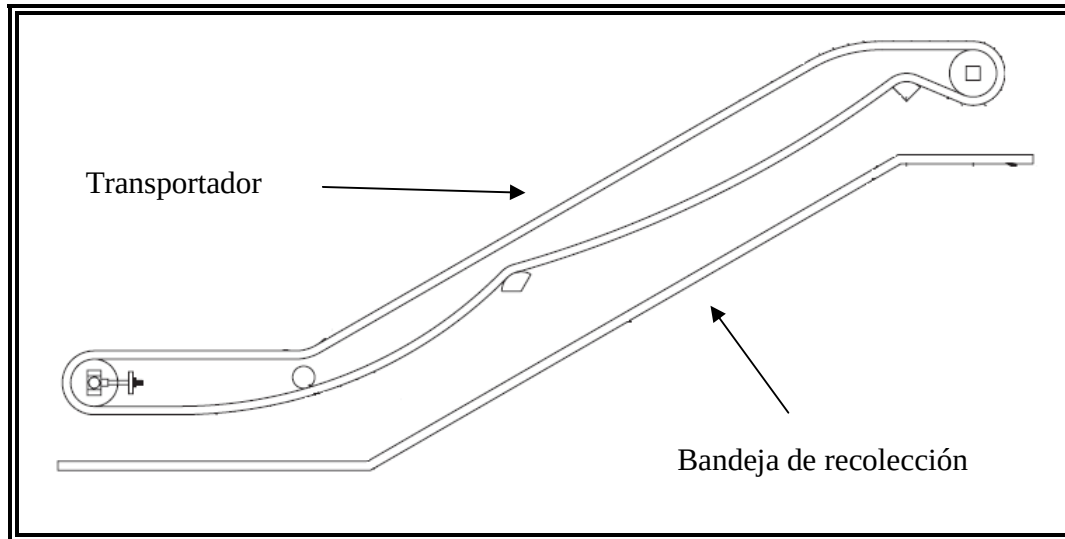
Detalle de la bandeja de recolección. Fuente: Elaboración propia.
